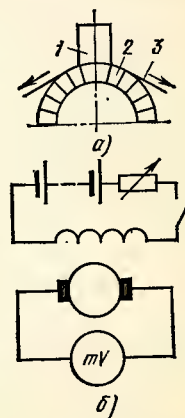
Притирка щеток (а) и схема отыскания нейтрали (б)
